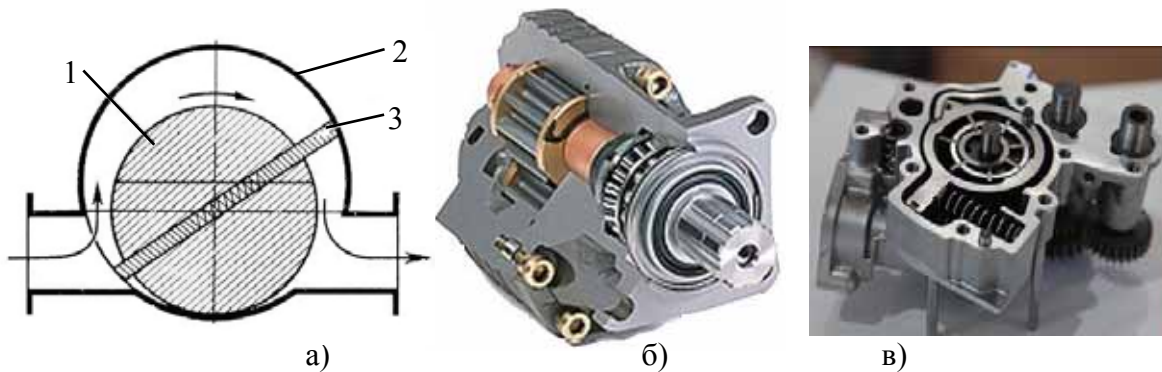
Конструкція (а) та зовнішній вигляд (б, в) пластинчастих насосів: 1 – ротор; 2 – корпус; 3 – пластини
